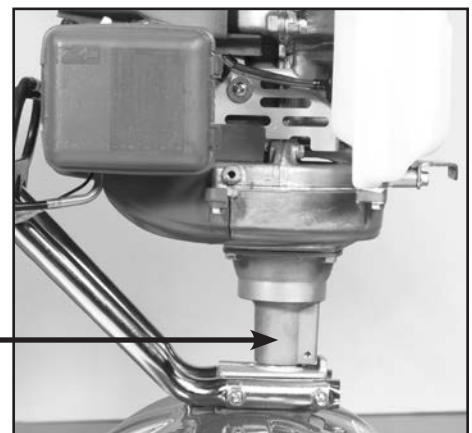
Der Motor liegt richtig auf dem Getriebe auf.
